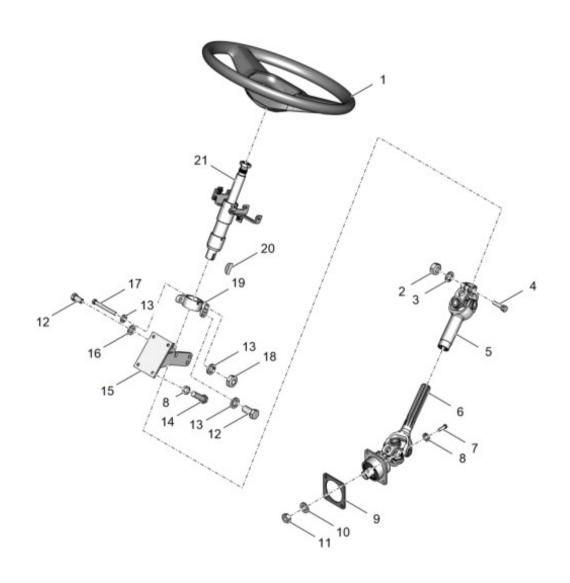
4320Ф-3400004-Установка рулевой колонки
